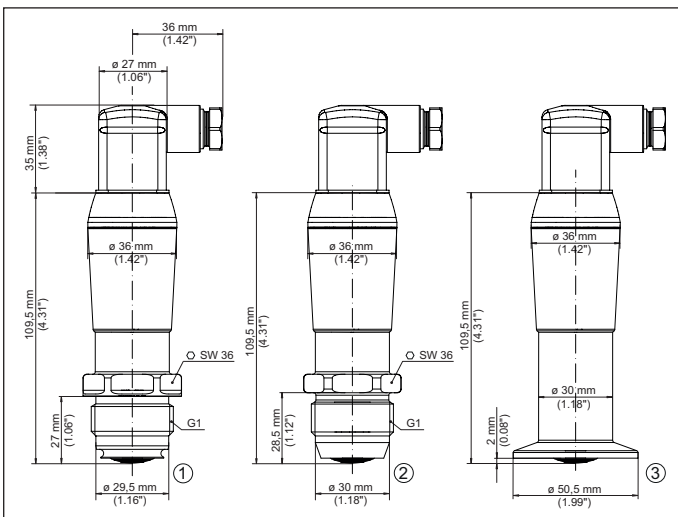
VEGAPOINT 24, Hygieneausführung - Gewinde mit ISO 4400-Stecker
